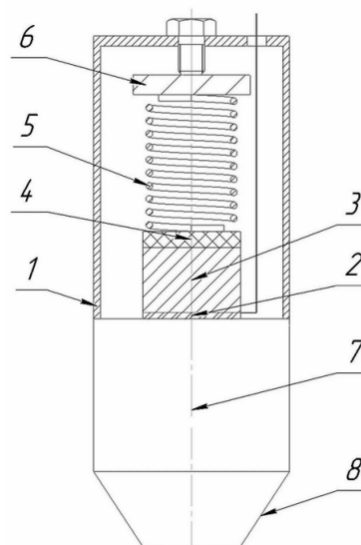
Конструкция высокотемпературного пьезоэлектрического преобразователя. 1 – корпус; 2 – пьезопластина; 3 – демпфер; 4 – слой электрической изоляции; 5 – пружина; 6 – подшипник; 7 и 8 – волновод
